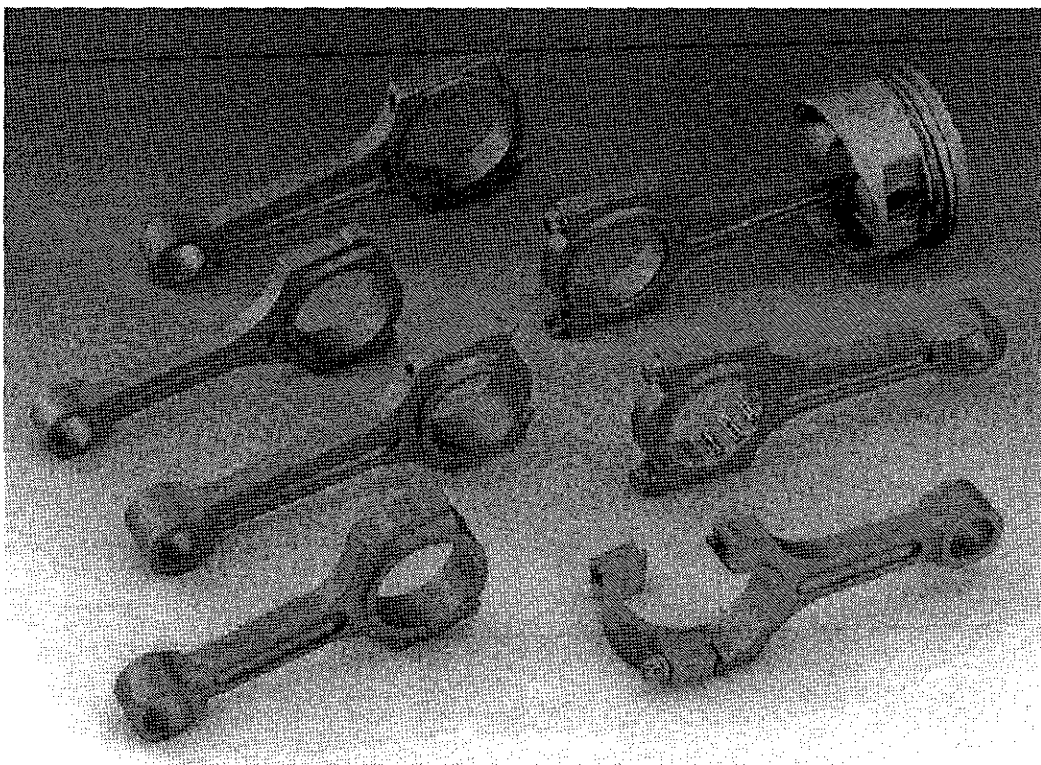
เปรียบเทียบความแตกต่างระหว่าง Axial Die Pressing, Forging และ Powder Forging
